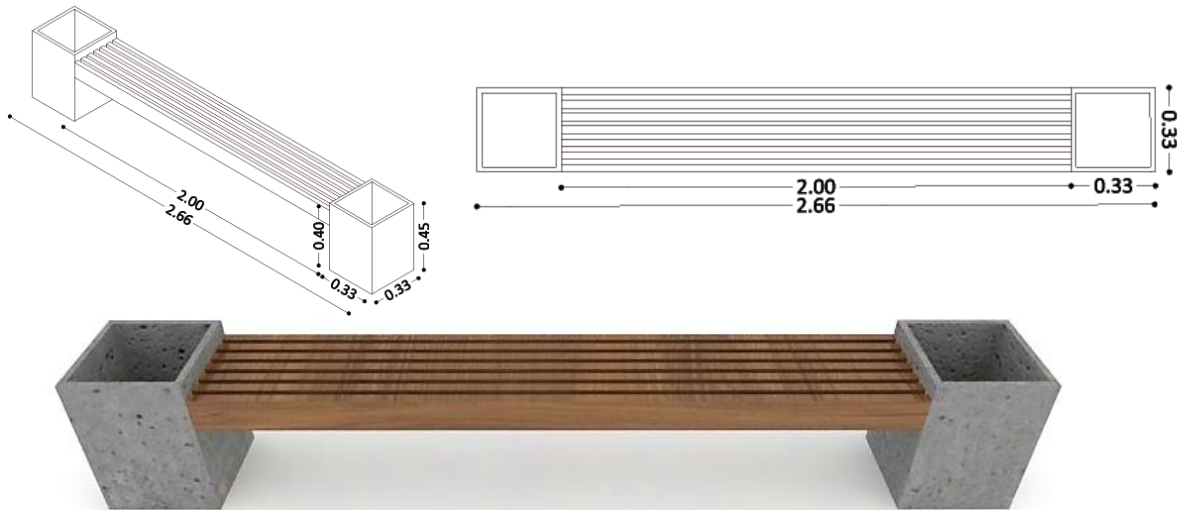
Planimetría y render, banca 3. Fuente: grupo de investigación.
